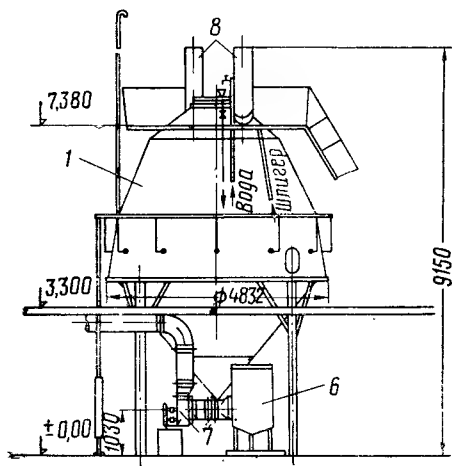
Общий вид распылительной сушилки ПКБ НИИСтройкерамики
